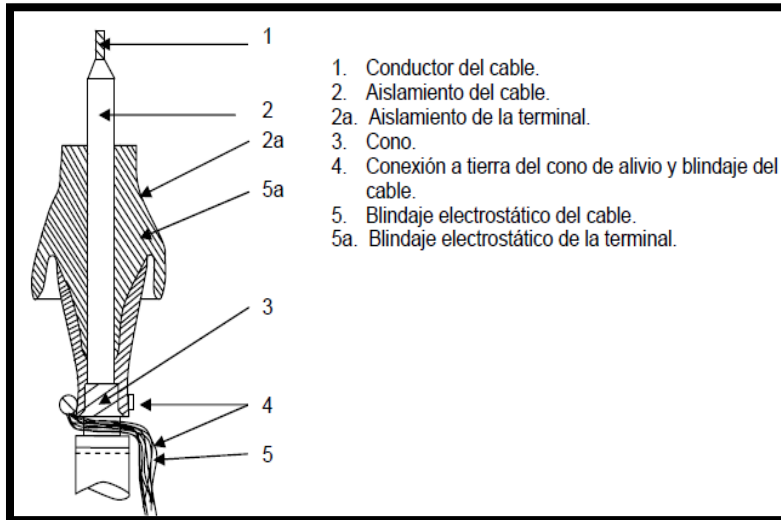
Detalle constructivo de la terminal para uso en interiores [19].
